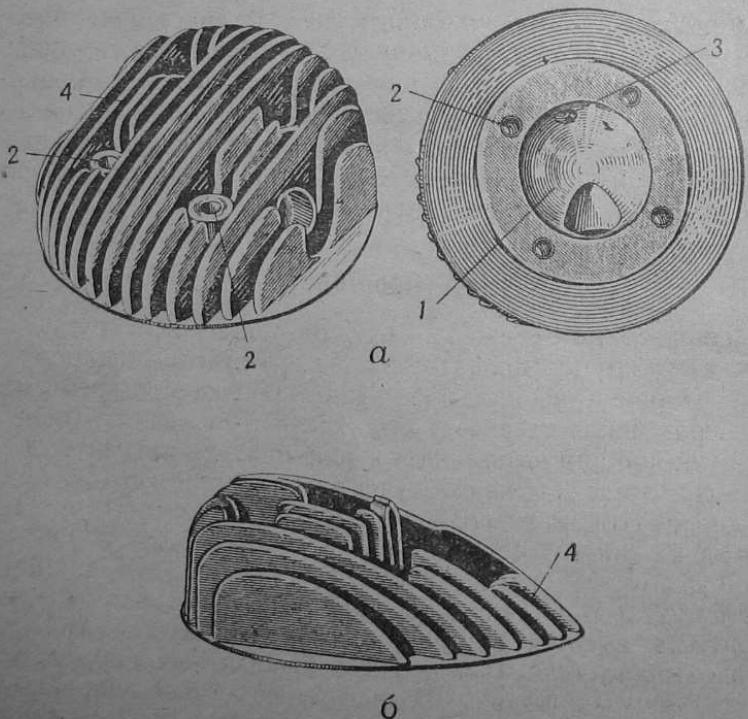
Головки цилиндра: а — двигателя ИЖ-49; б — двигателя М1А:
